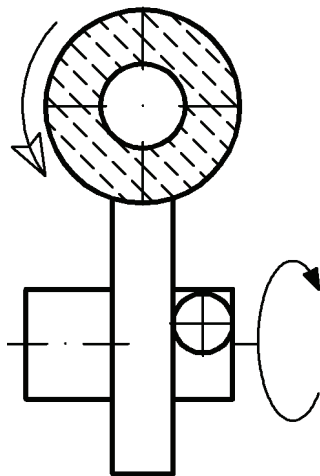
Схема способа зачистки отливок: зачистка цилиндрической поверхностью периферией абразивного круга
